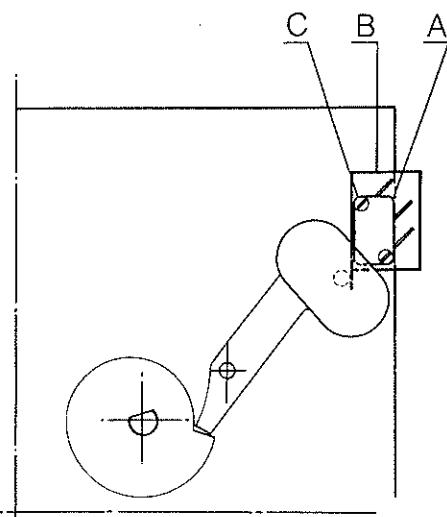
Montaggio contatto di segnalazione molle cariche
